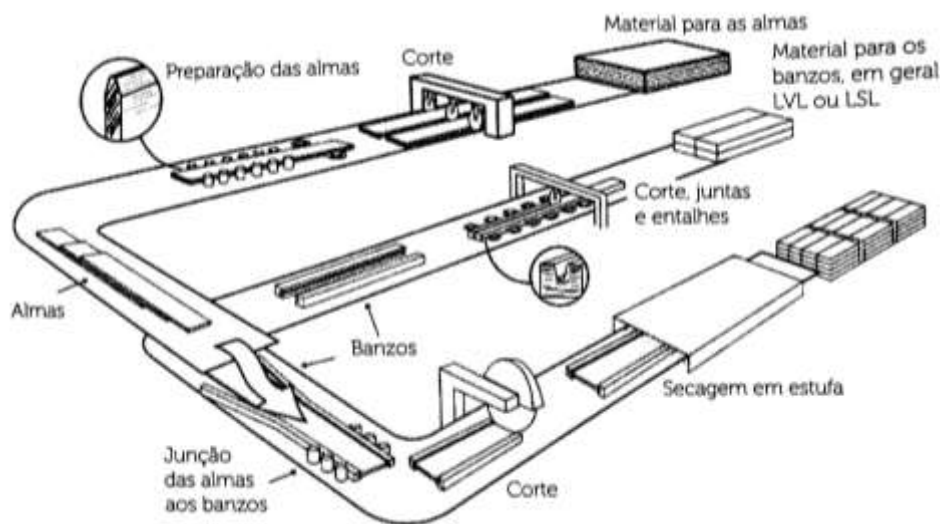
Produção de vigas I. Autor: Paulo Barreto Cachim
